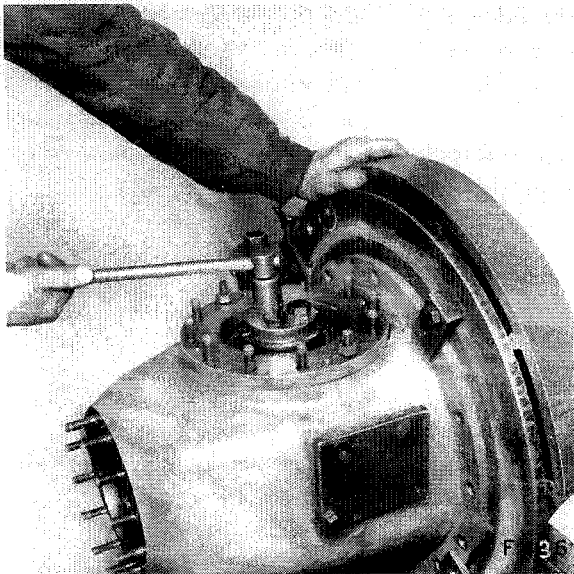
Lösen der Befestigungsschrauben auf der Welle des Stirnradkolbens
